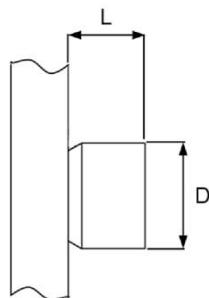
Griptec Anschweißmuffe (GW)
